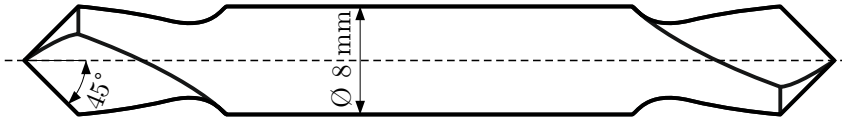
Exemplarische Darstellung eines Fräswerkzeugs
